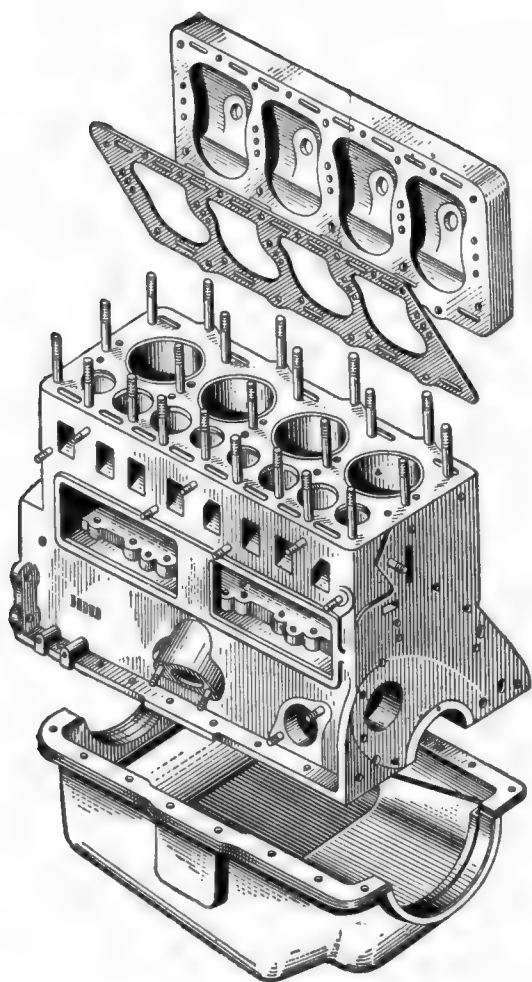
Блок, картер и головка цилиндров с прокладкой
